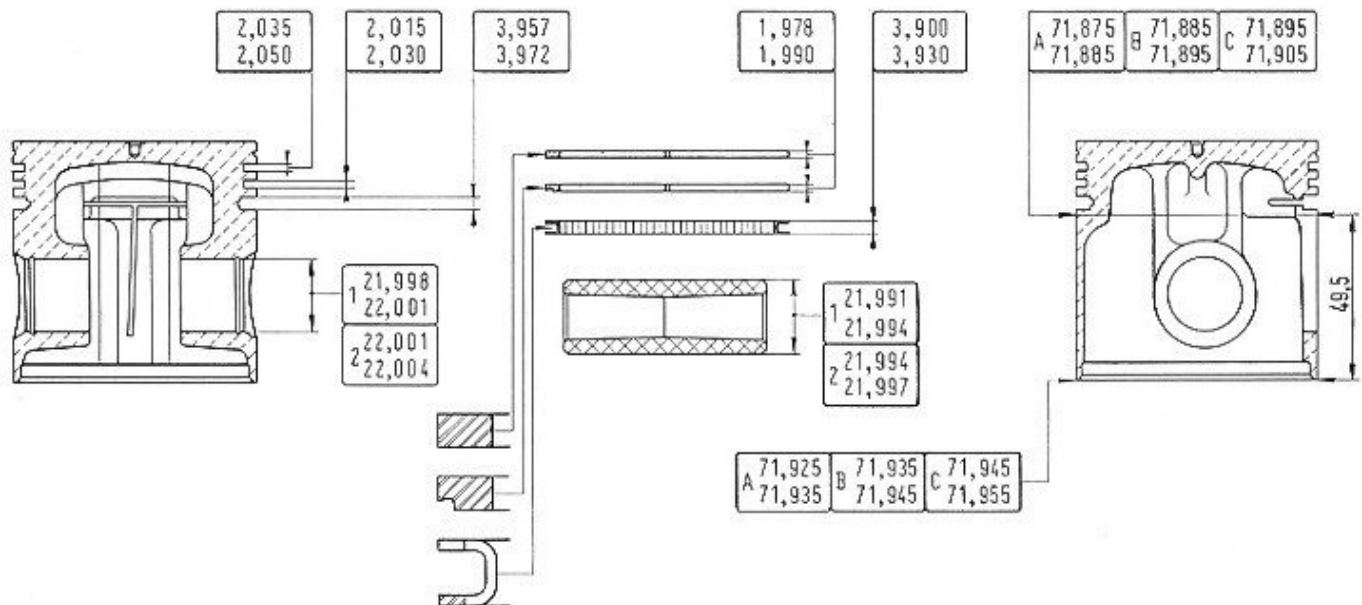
Wichtigste Daten für die Kolben, die Kolbenbolzen und die Kolbenringe.
